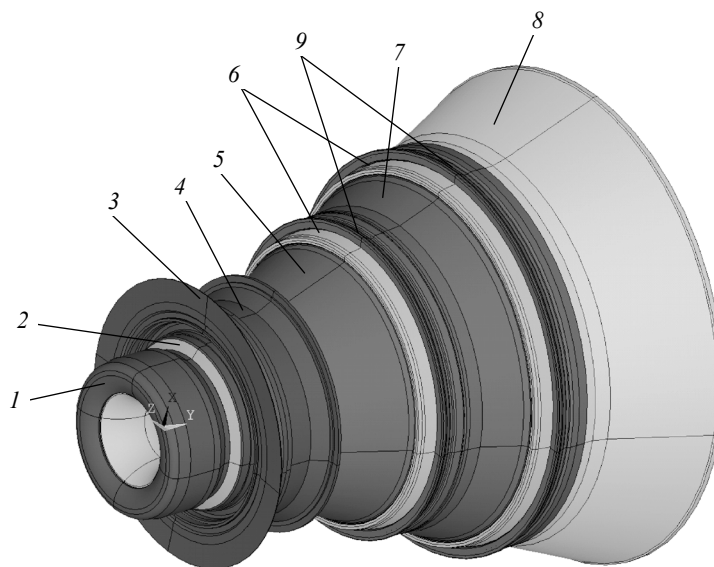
Поворотное-управляющее сопло (ПУС): 1 – входная часть сопла; 2 – эластично-опорный шарнир (ЭОШ); 3 – фланец; 4 – силовой корпус; 5 – раструб поворотный (РП); 6 – цапги; 7 – внутренний выдвигной насадок (ВВН); 8 – наружный выдвигной насадок (НВН); 9 – шпангоут
